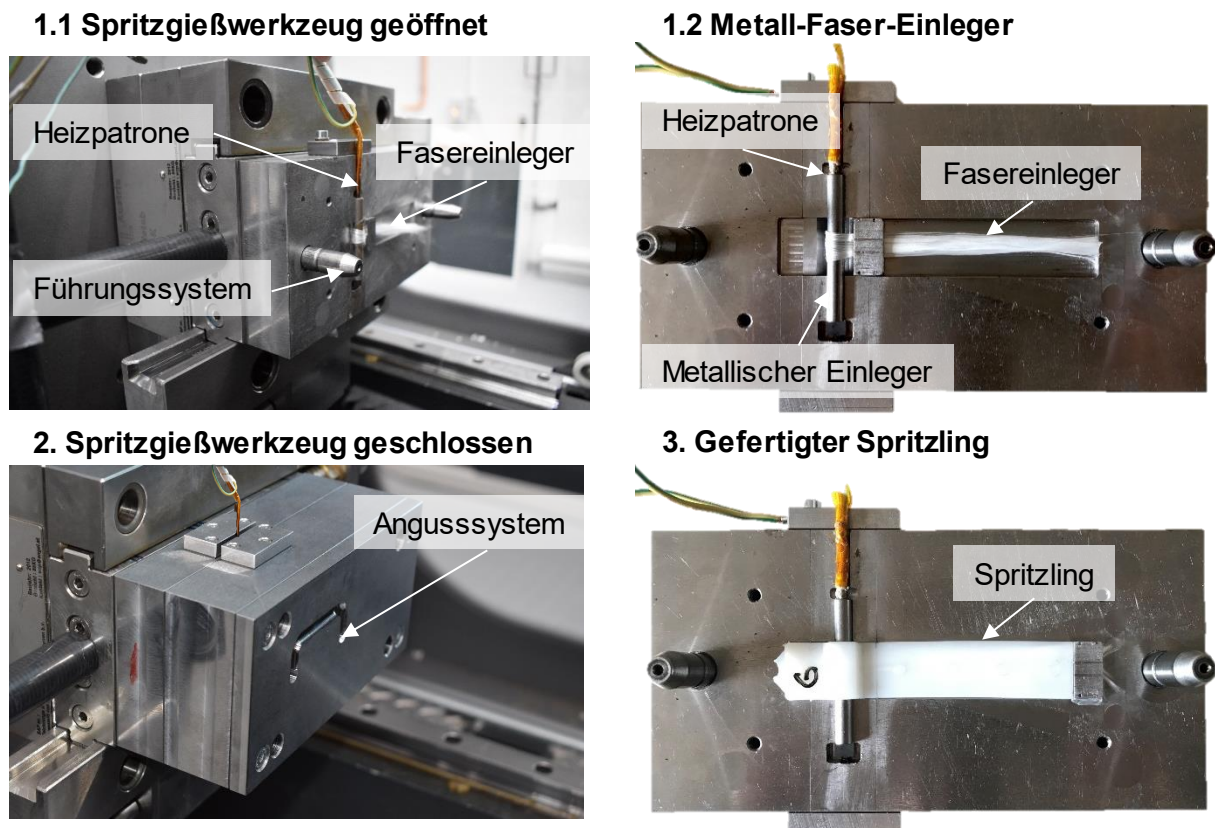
Spritzgießwerkzeug und experimenteller Prozessablauf
